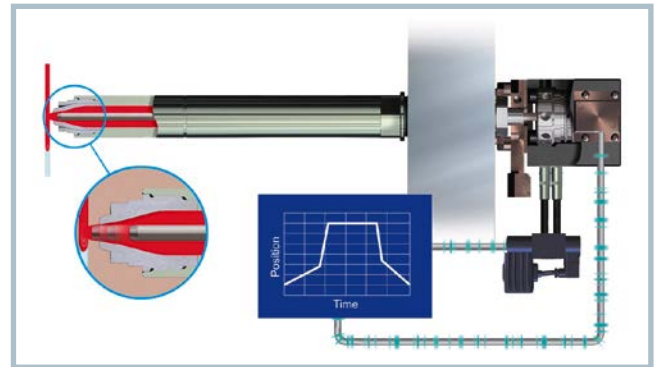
Hydraulisch betriebenes Nadelverschlussystem mit präziser Hubstellung und -überwachung (© Synventive)
